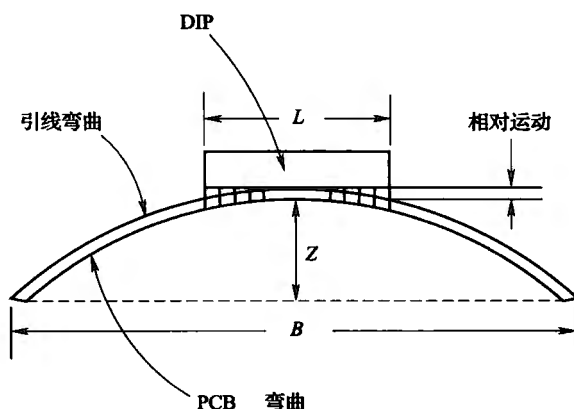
PCB 谐振时因元器件和 PCB 间的相对运动而在导线上产生应力
